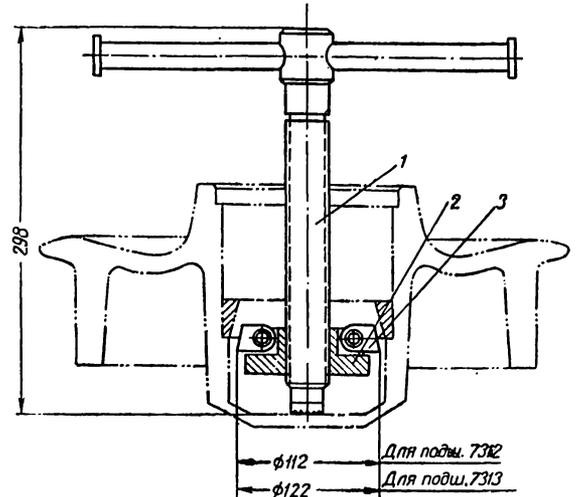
Съемник колец подшипников из колес вагонеток грузоподъемностью более 1 т
